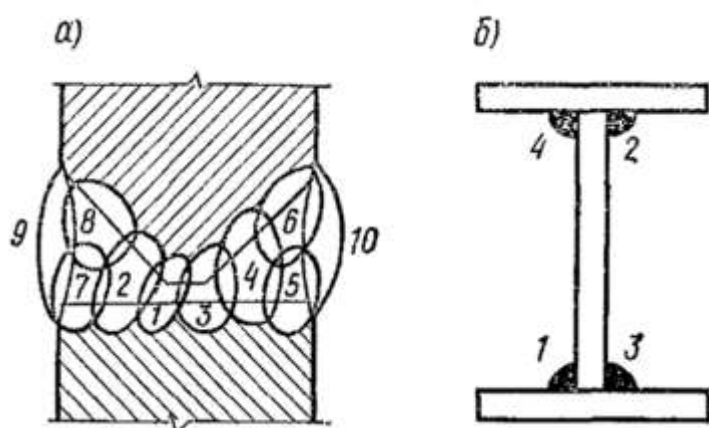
Чередование швов: а — при сварке двустороннего шва; б - при сварке поясных швов балки; 1-10- последовательность швов.
